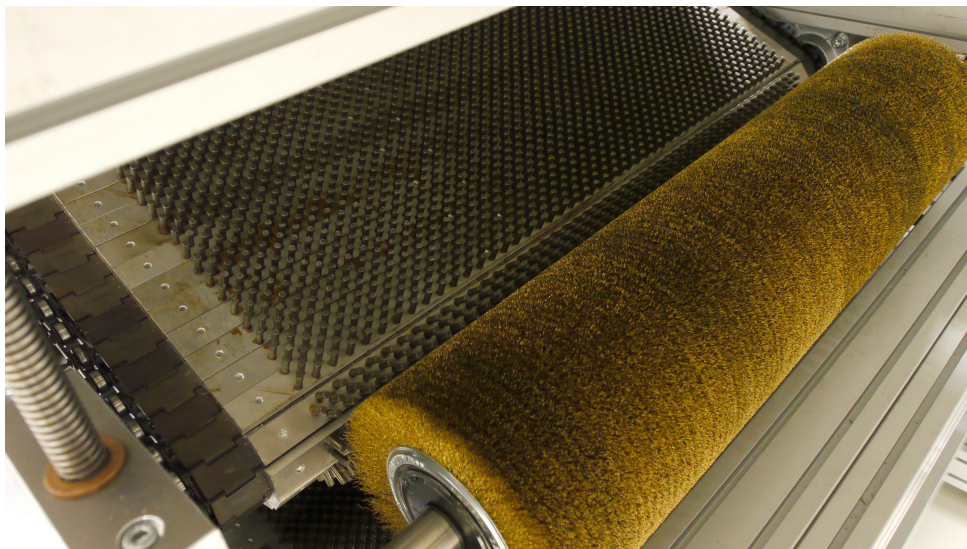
Messingbürste zur Reinigung der formgebenden Werkzeugelemente
